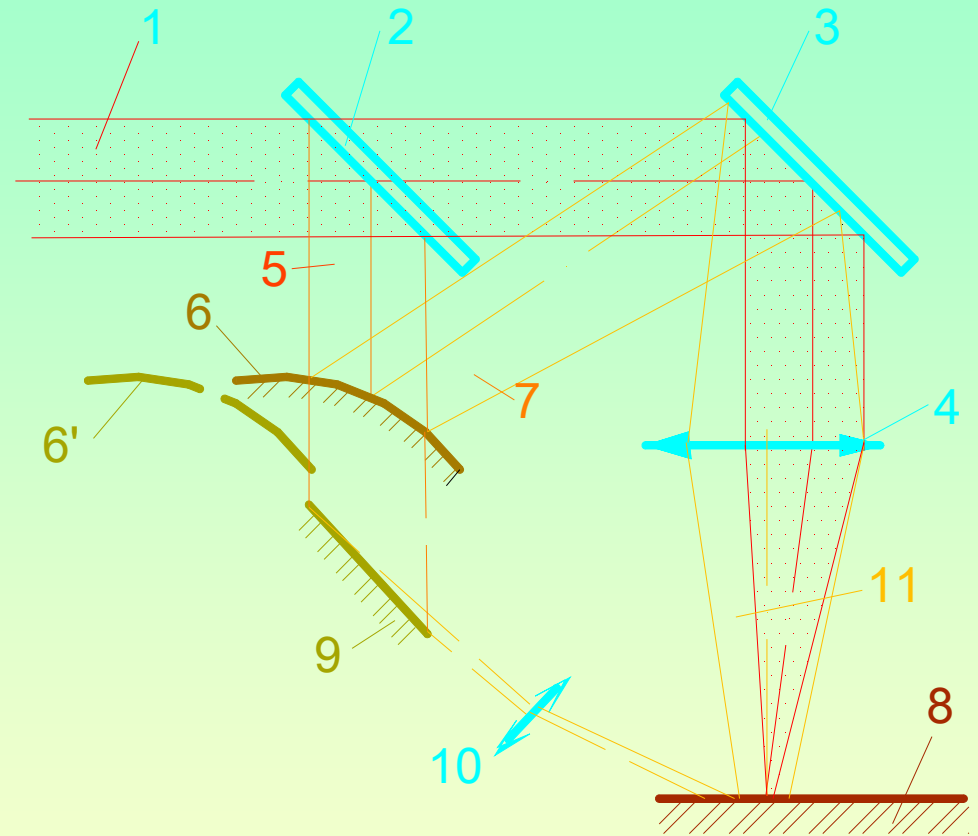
Схема лазерного вирізання пазів підігрівом поверхні заготовки
